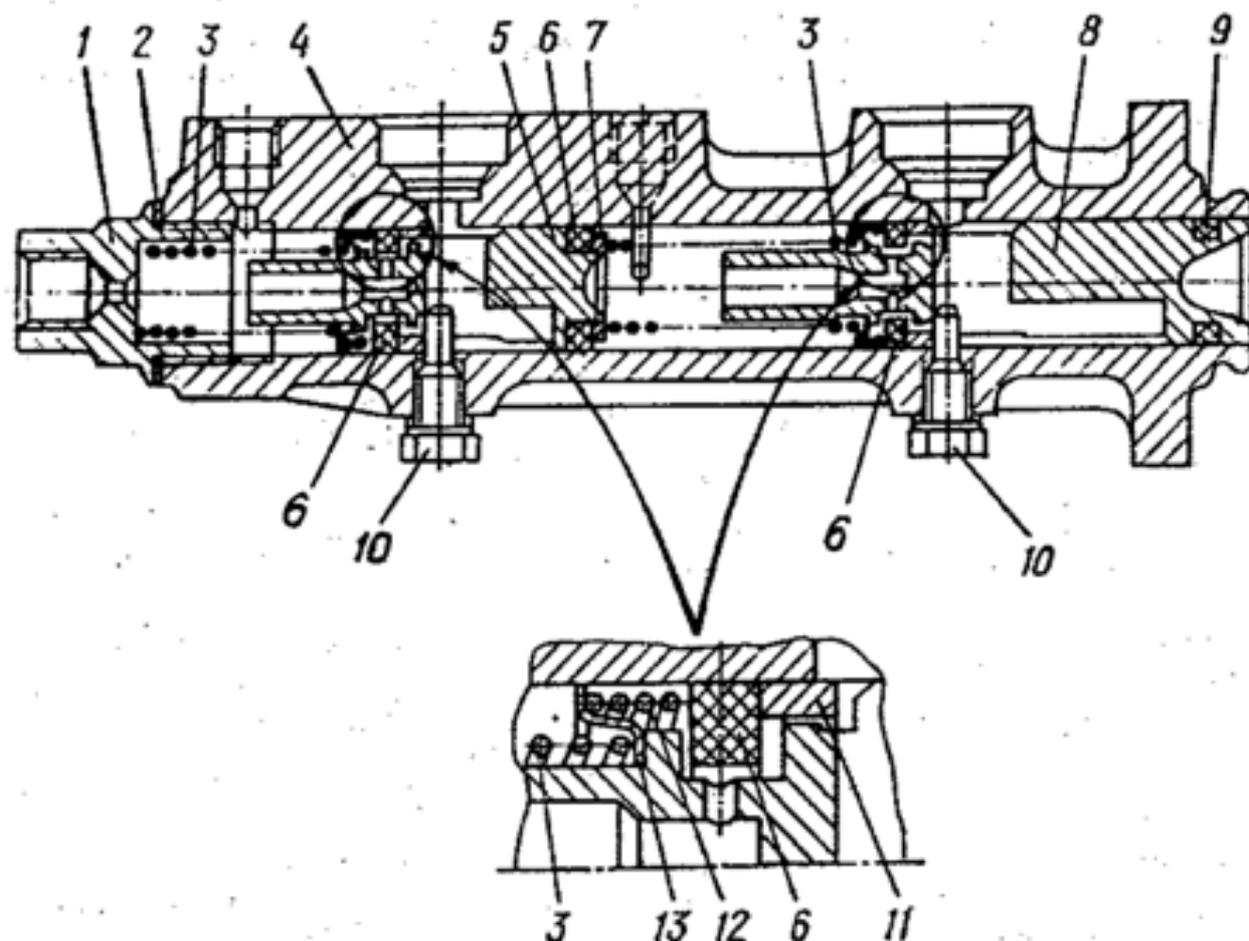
Главный тормозной цилиндр: 1 - пробка; 2 - прокладка; 3 - пружина поршня; 4 - цилиндр; 5 - поршень задней полости; 6 - манжета уплотнительная высокого давления; 7 - шайба упорная; 8 - поршень передней полости; 9 - манжета уплотнительная низкого давления; 10 - болт установочный; 11 - втулка распорная; 12 - пружина чашки; 13 - чашка.
